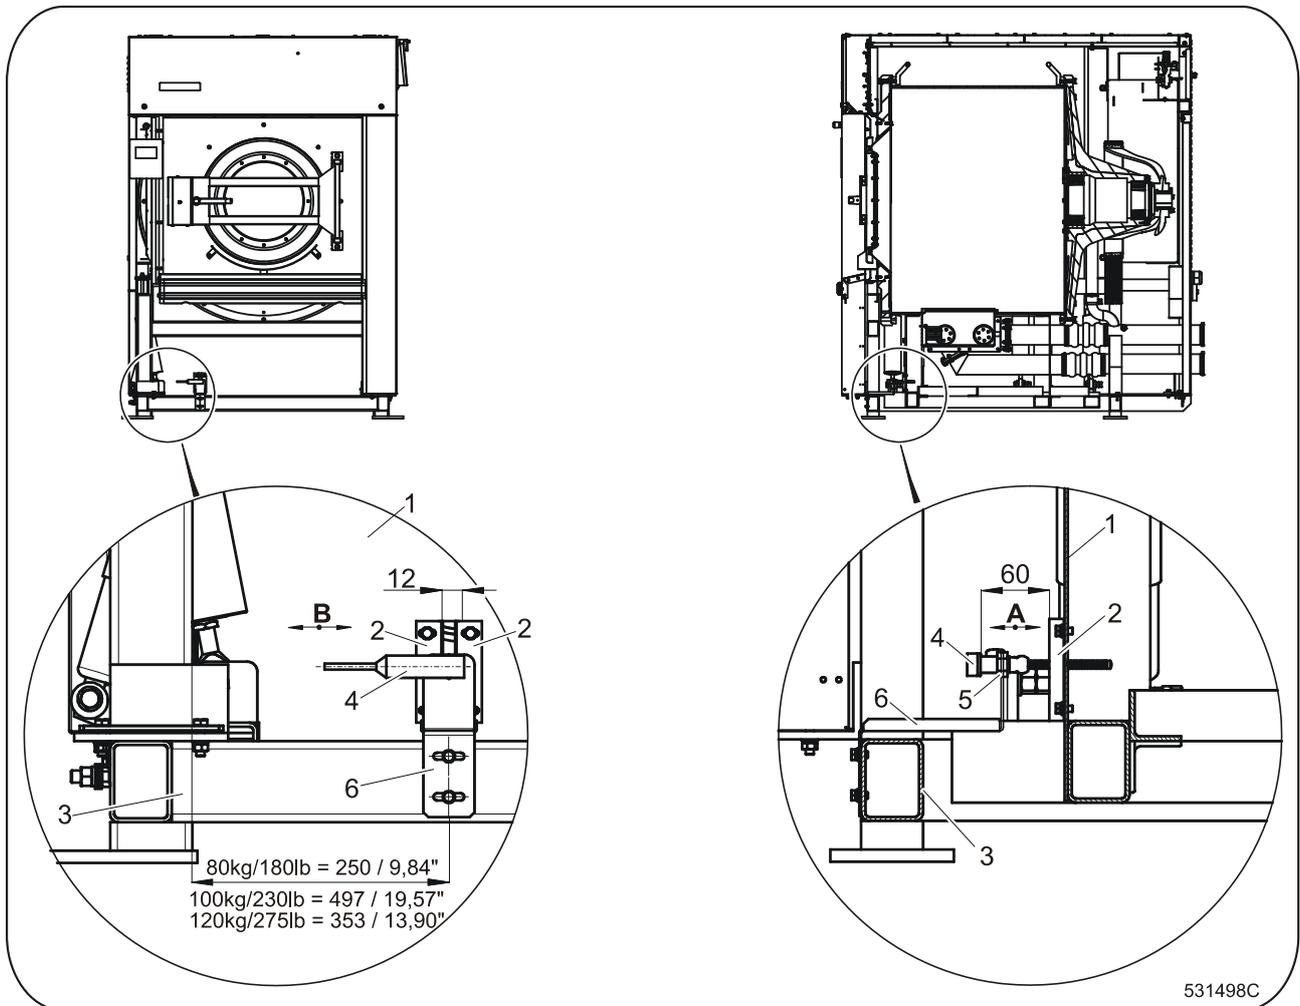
B Máquinas 80-100-120 kg / 180-230-275 lbs, (dimensiones en mm / pulgada)
